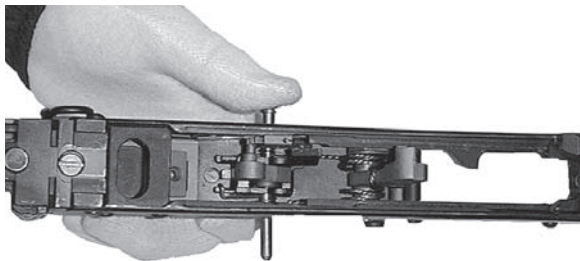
Przyłączanie mechanizmu przerywacza serii
